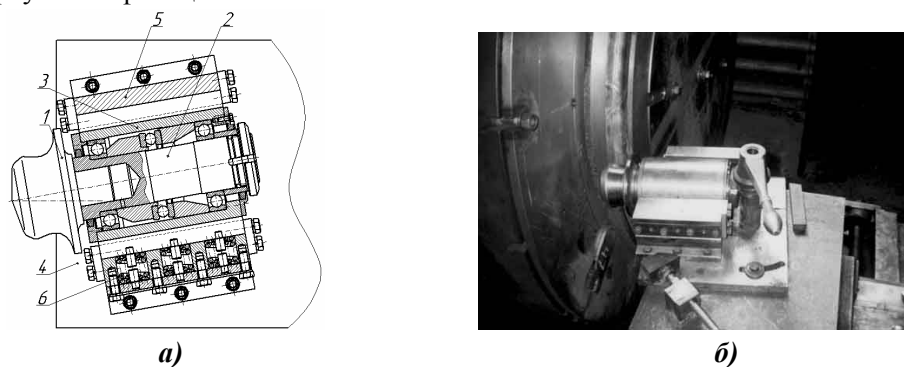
Конструкція розкочувальної головки (а) і загальний вигляд розкочувальної 1 – валок; 2 – вісь; 3 – втулка; 4 – супорт верстата; 5 – утримувач; 6 – пружина приставки до лобового токарного верстата (б)
